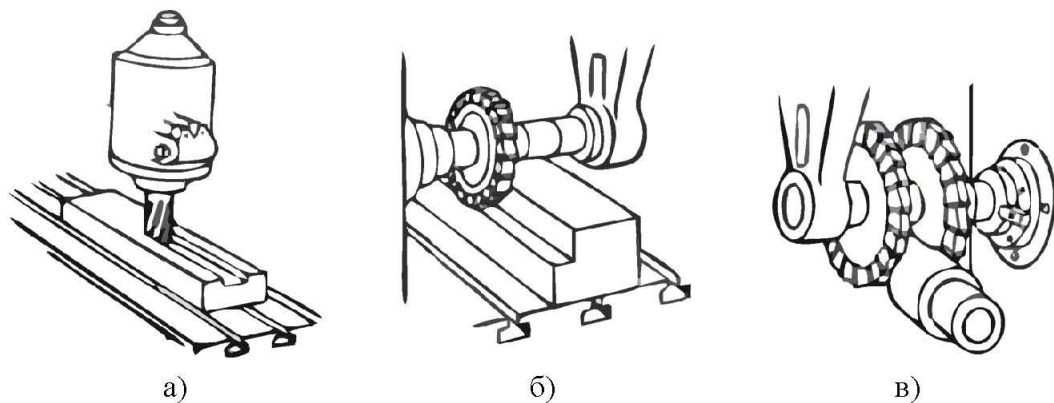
Фрезерування пазів та виступів: а – паза кінцевою фрезою, б – виступу дисковою трьохсторонньою фрезою, в – набором з двох дискових трьохсторонніх фрез
